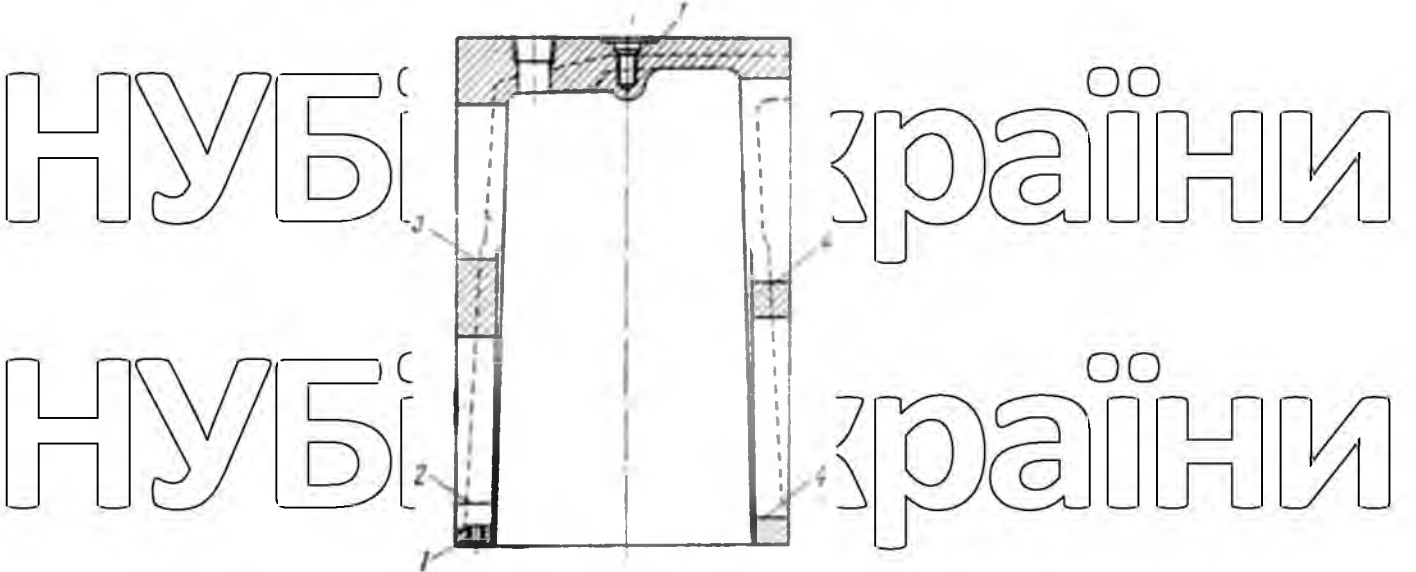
Корпус редуктора ВВП 17221.41.101-4. Схема дефектів
